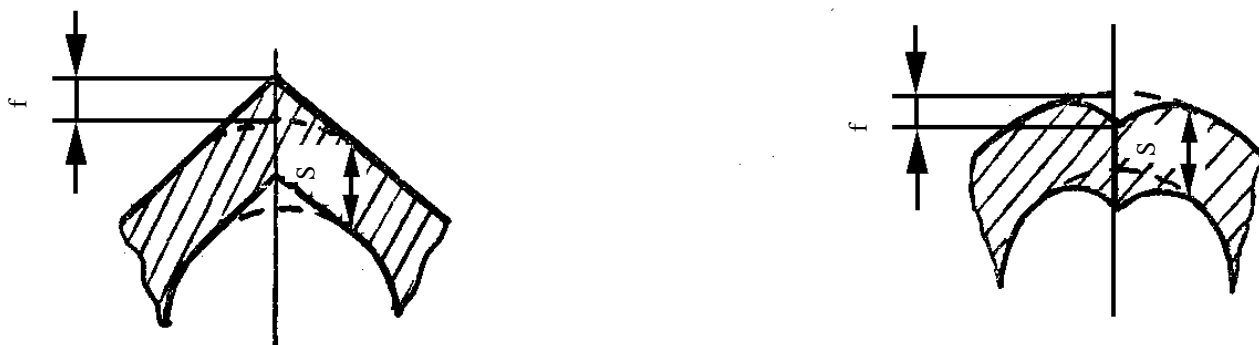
Увод (угловатость) кромок в сварных швах
